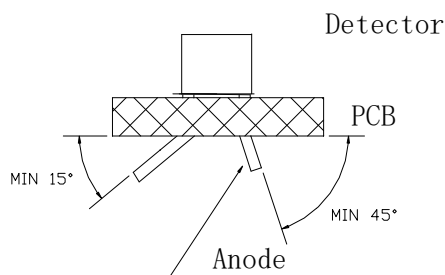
引脚与 PCB 夹角 Figure 11 angle between lead and PCB
